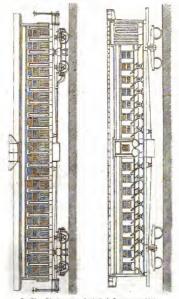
Élévation et coupe longitudinale d'un waggon américain.
